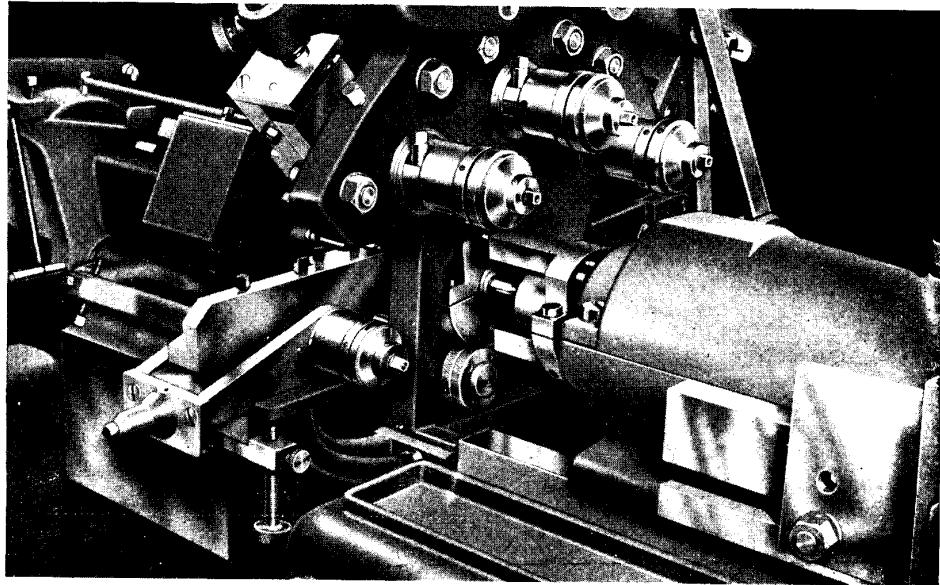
SEITENANSICHT DER FÜHRUNGSBÜCHSE DES DREHSTÄNDER-AUTOMATEN BP-U7
